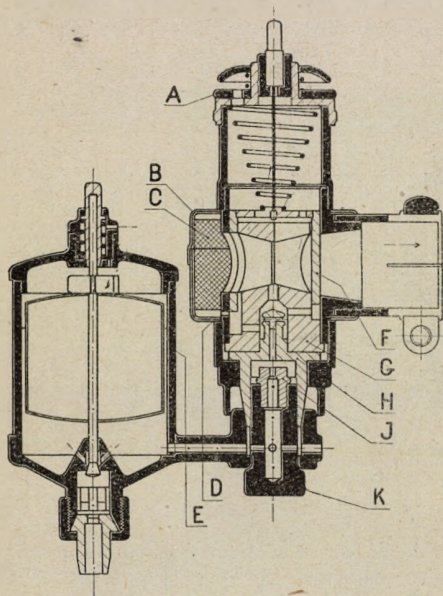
Vačkové regulační ústrojí starších karburátorů „Schebler“.
